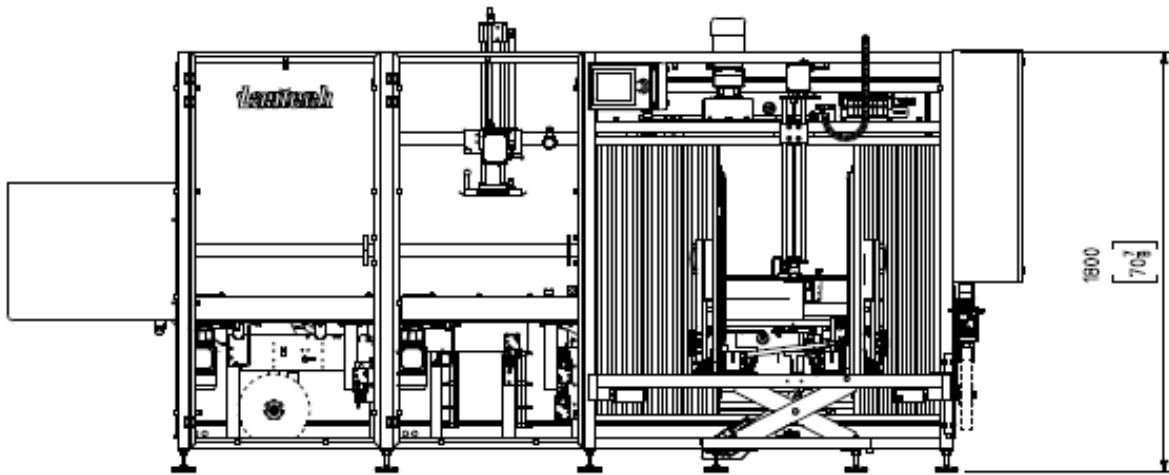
Plano de dimensiones de alto de armadora LANTECH
